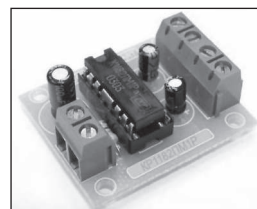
Внешний вид устройства плавного зажигания ГЛН
